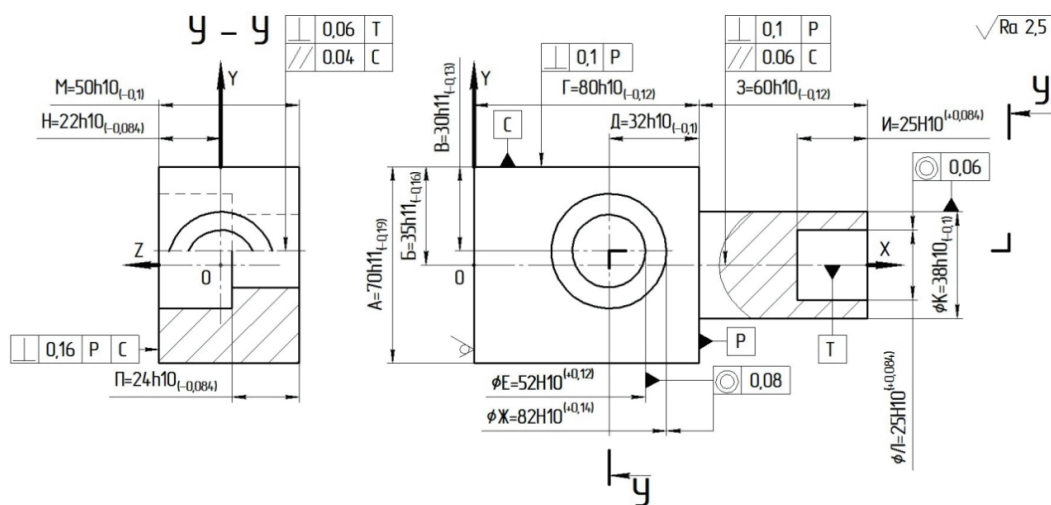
Преобразованный рабочий чертеж детали для размерного анализа
